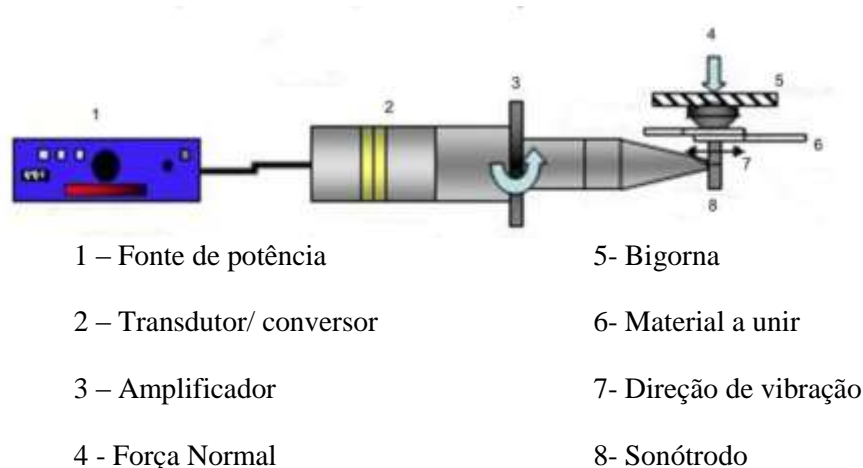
Equipamento de soldadura por ultrassons *Lateral Drive* [22]
